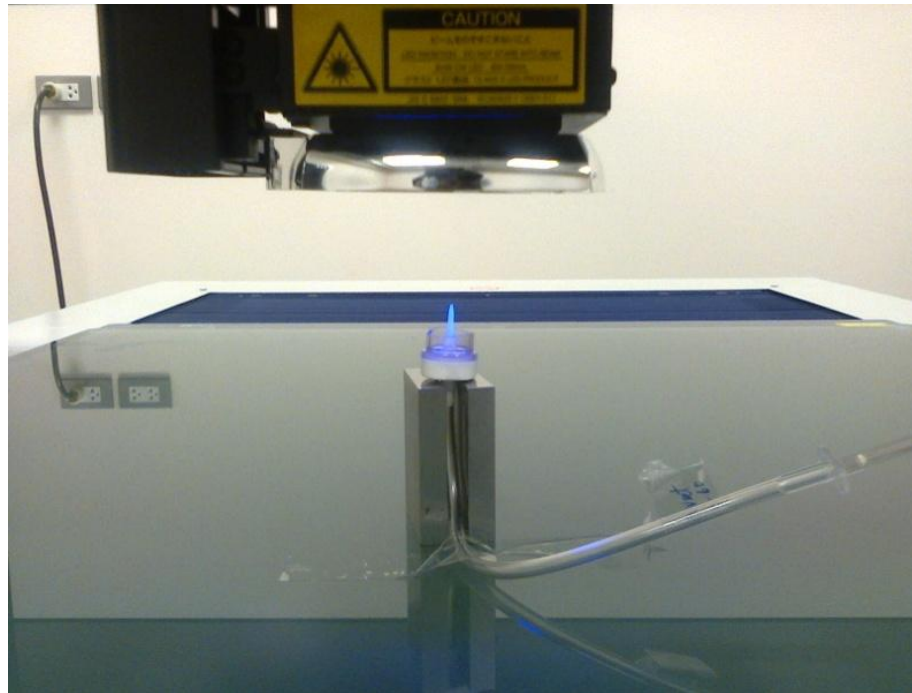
การแสดงผลของเครื่อง CNC Vision Measuring Machine สำหรับ IV Set 20 no.3
